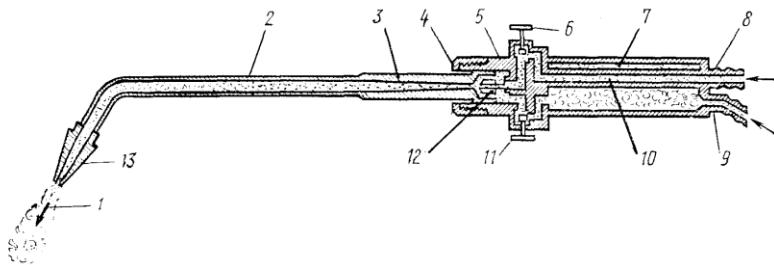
Схема инжекторной горелки: 1 – горючая смесь; 2 – трубка наконечника; 3 – смесительная камера; 4 – накидная гайка; 5 – корпус горелки; 6 – вентиль для кислорода; 7 – ацетиленовый канал; 8 – кислородный ниппель; 9 – ацетиленовый ниппель; 10 – кислородная трубка; 11 – вентиль для ацетилена; 12 – инжектор; 13 – мундштук
